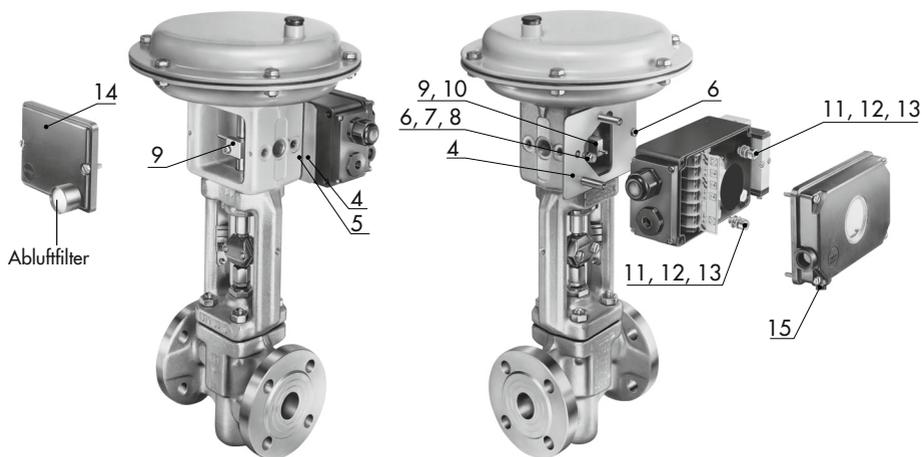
Montage an SAMSON-Hubantriebe Typ 3277
